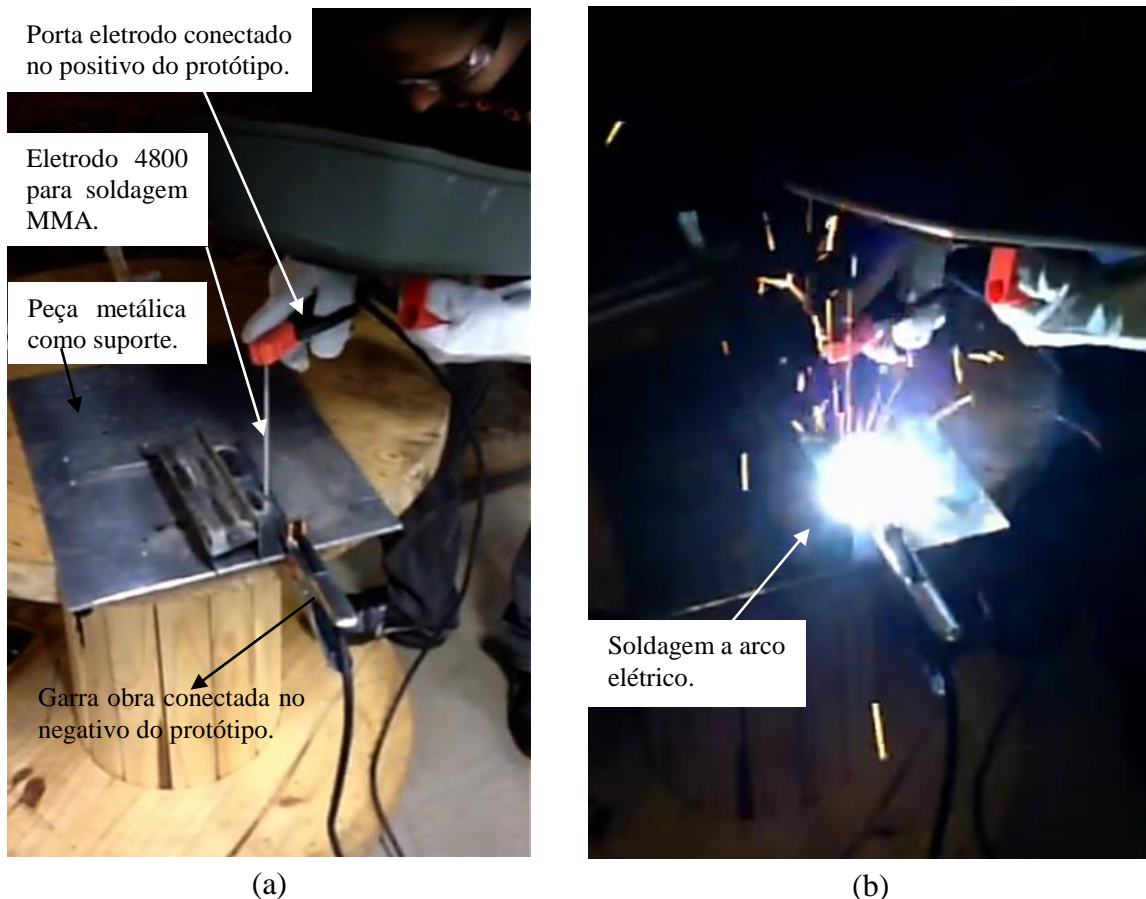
(a) bancada utilizada para realizar o teste de soldagem no processo MMA; (b) arco elétrico de soldagem.
